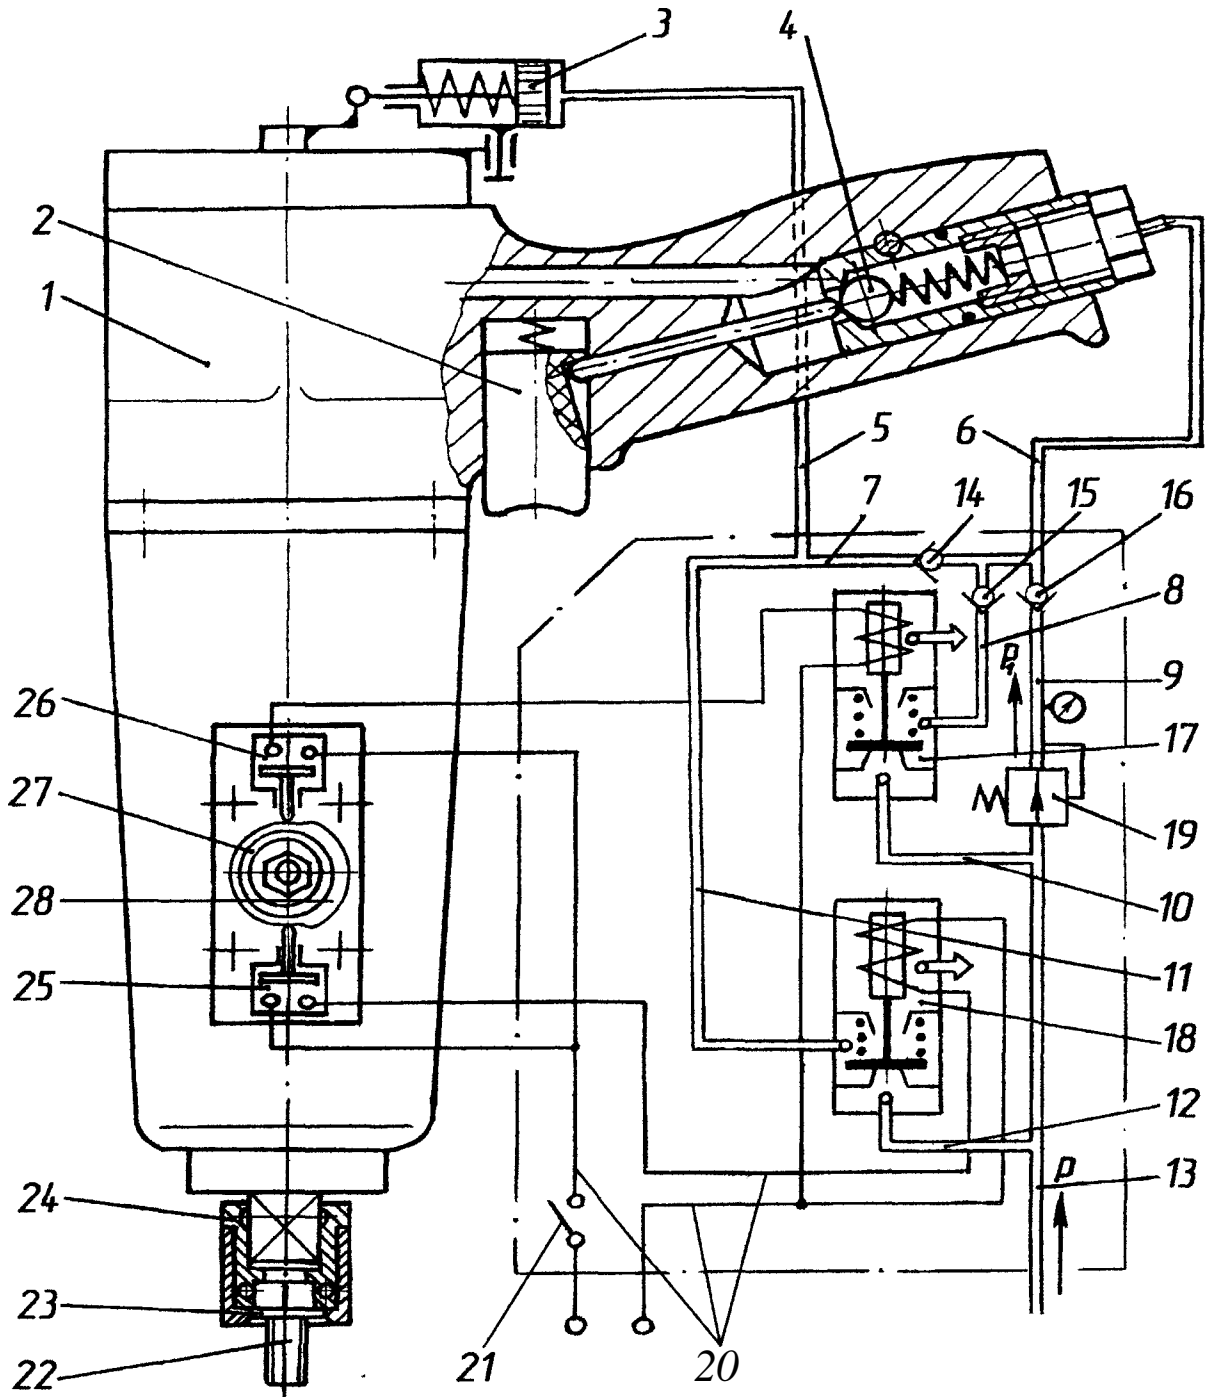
22 – Ручний пневматичний адаптивний гайкоокрут
